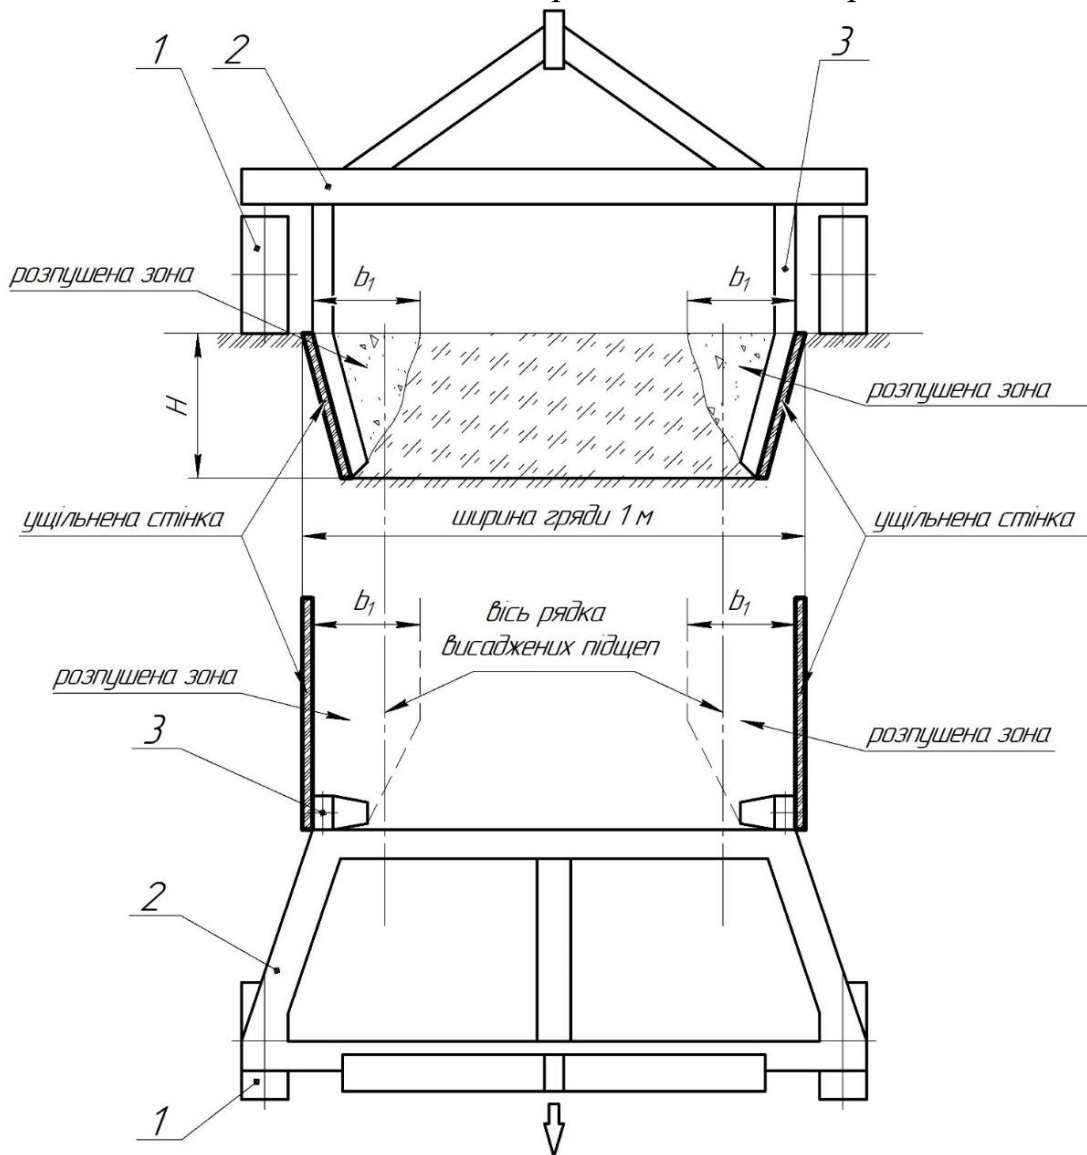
Конструктивно-технологічна схема глибокорозпушувача для створення контуру смугової гряди: 1 – колесо опорне; 2 – рама; 3 – робочий орган;  $H$  – глибина смугової гряди;  $b_1$  – ширина зони розпушення.
